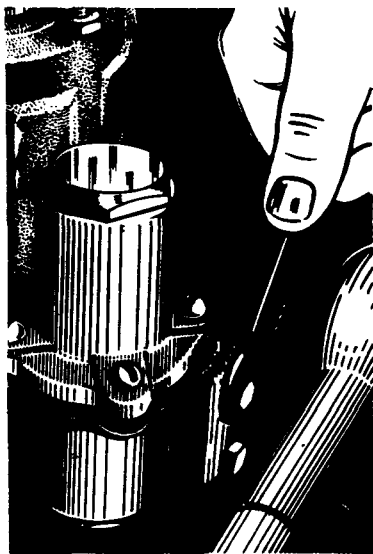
Отвертывание болта крепления регулятора к компрессору
